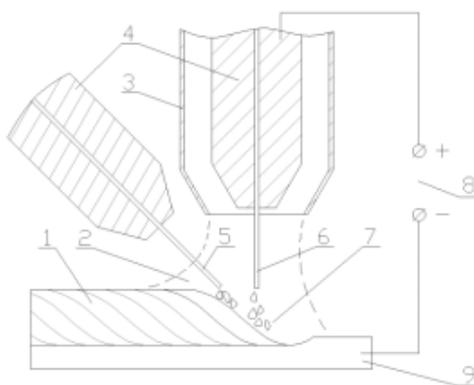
Схема процесса сварки в защитных газах с дополнительной подачей присадочной проволоки
